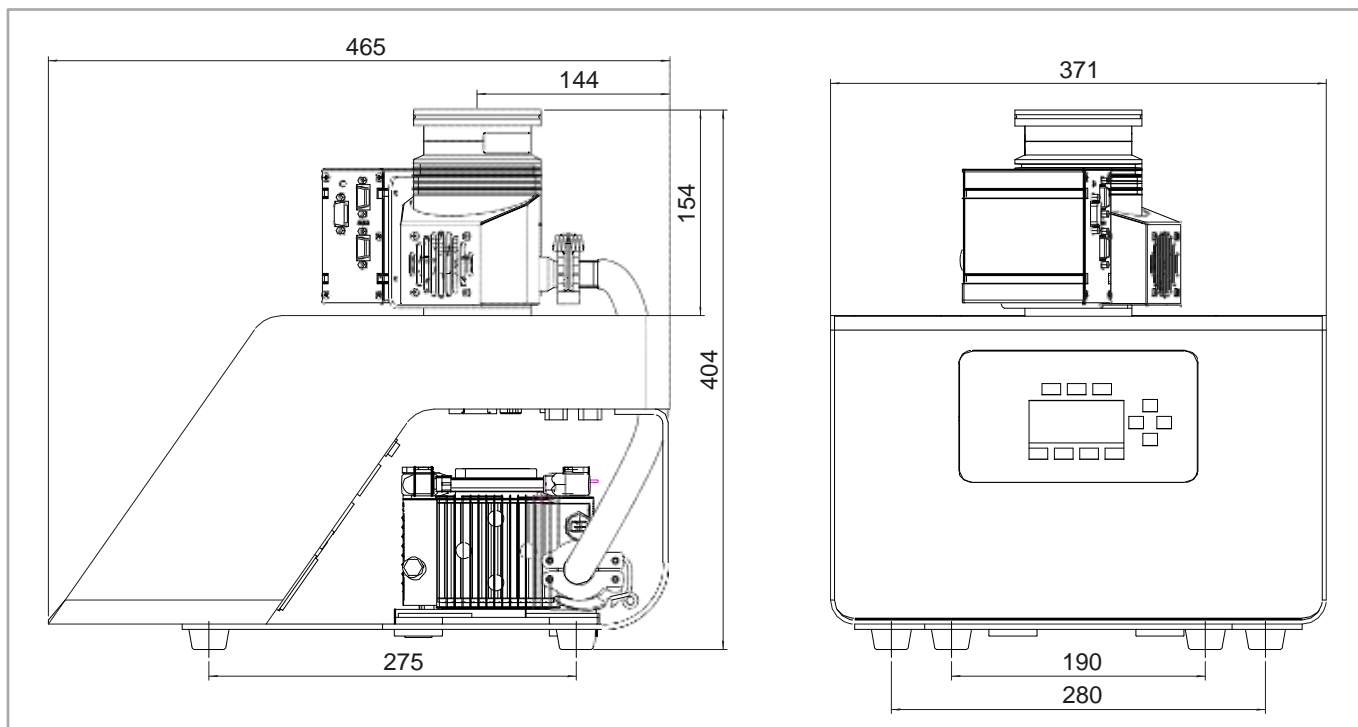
Габаритные размеры TURBOLAB 80, размеры в мм
